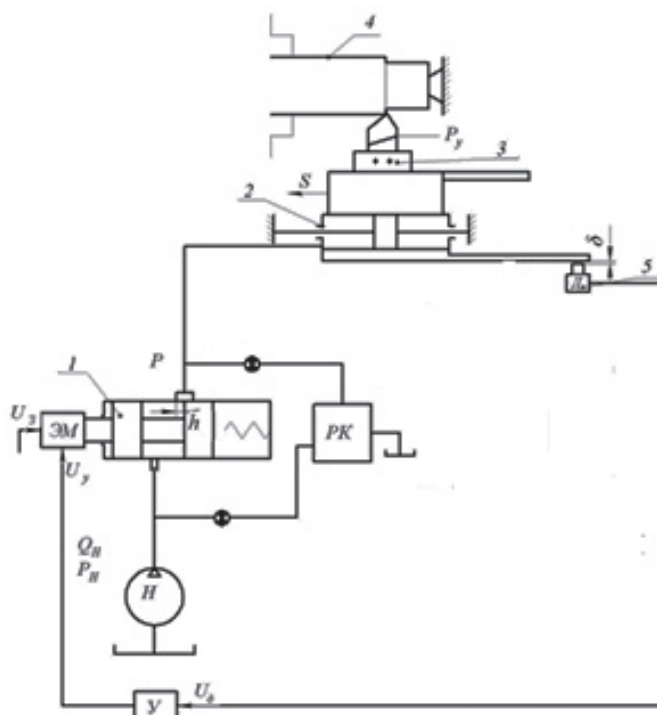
Принципиальная схема автоматической системы стабилизации подачи инструмента при токарной чистовой обработке. Н – насос силового цилиндра; РК – редукционный клапан; P_y – сила резания; S – подача инструмента; q – зазор гидростатической направляющей; h – величина открытий рабочей щели; Q_n , P_n – расход и давление насоса; I_z – задающий сигнал; I_d – сигнал датчика; I_y – сигнал усилителя; 1 – регулятор расхода силового цилиндра; 2 – силовой цилиндр; 3 – суппорт; 4 – обрабатываемая деталь; 5 – индуктивный датчик
